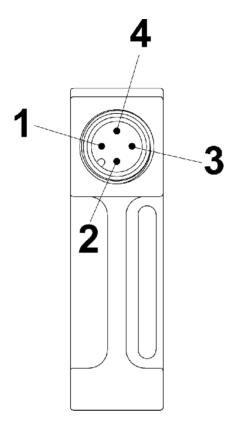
Pin-Belegung Gerätestecker M12x1 (Form 15x50)
